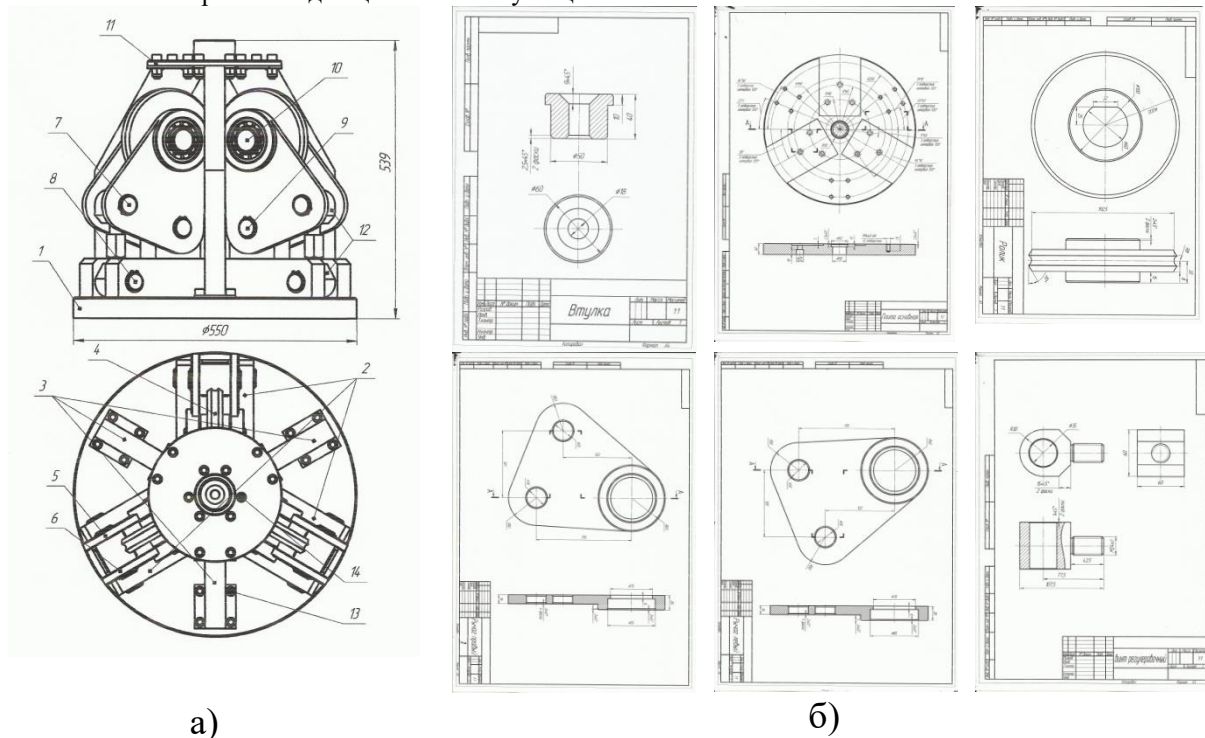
Конструкція пристосування для обтиснення трубчастої заготовки між роликами:
